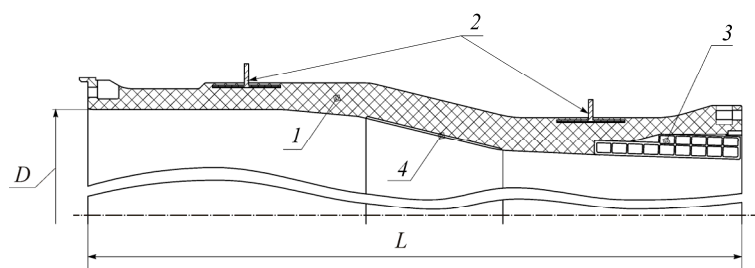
Конструкция органопластикового корпуса: 1 – полимерная композитная оболочка; 2 – металлические шпангоуты; 3 – панель шумоглушения; 4 – прирабатываемое покрытие
